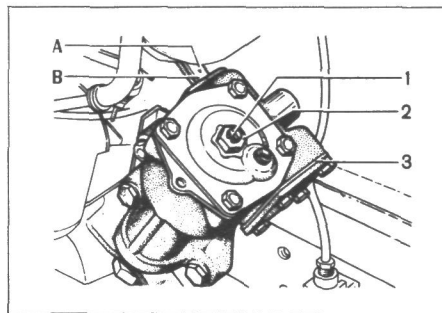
Регулировка зазоров в рулевом механизме: 1 — винт; 2 — гайка; 3 — регулировочные прокладки; А и В — метки
